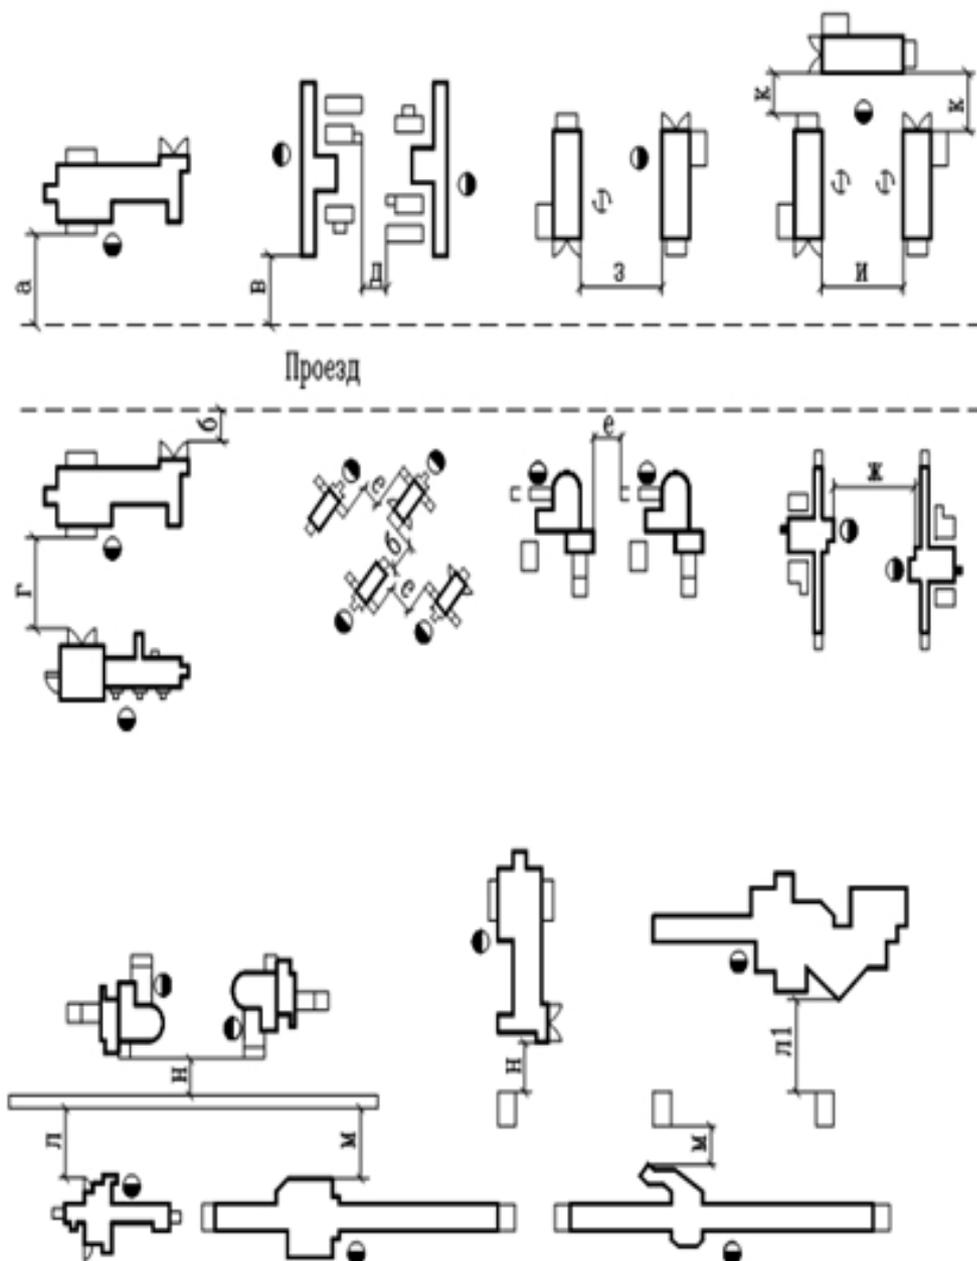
Нормы расстояний универсальных станков от проезда, относительно друг друга от стен и колонн здания
